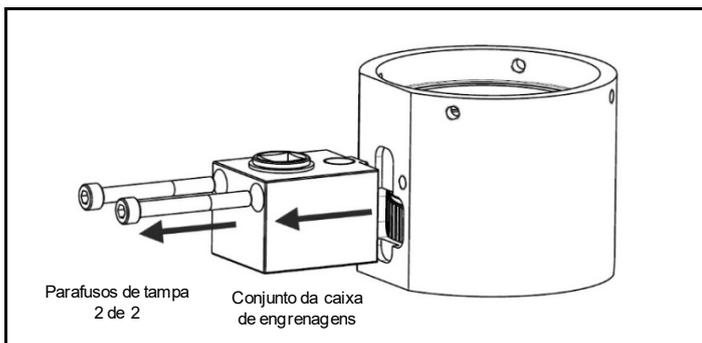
Separação do conjunto montagem da ponte e do conjunto da caixa de engrenagens
